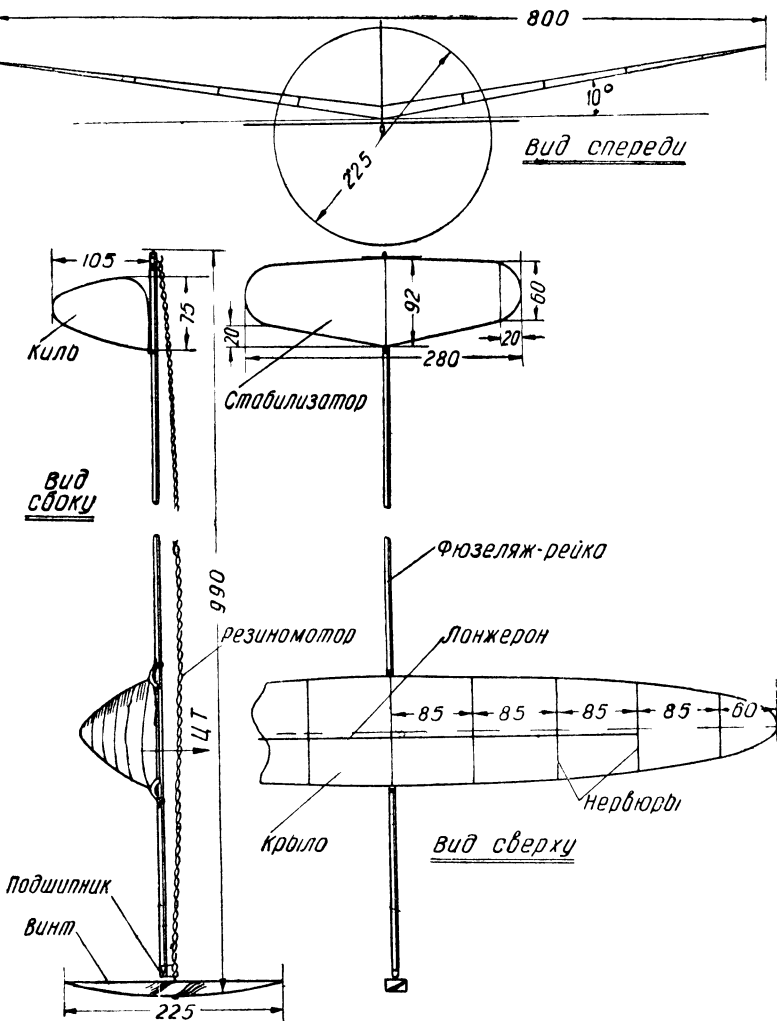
Общий вид схематической летающей модели тракторного типа конструкции Лесика Нестеренко
